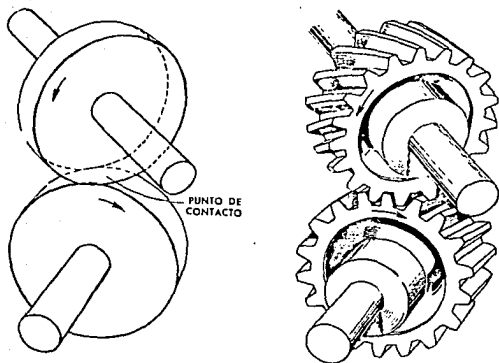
Engranés helicoidales de ejes cruzados.
